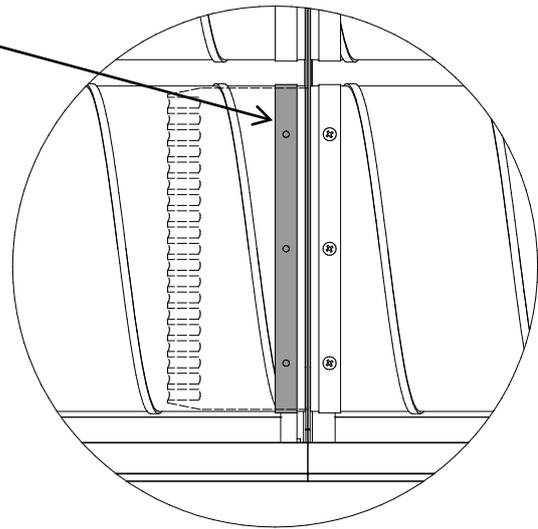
Blocage manchon-tube (vue de dessous)
